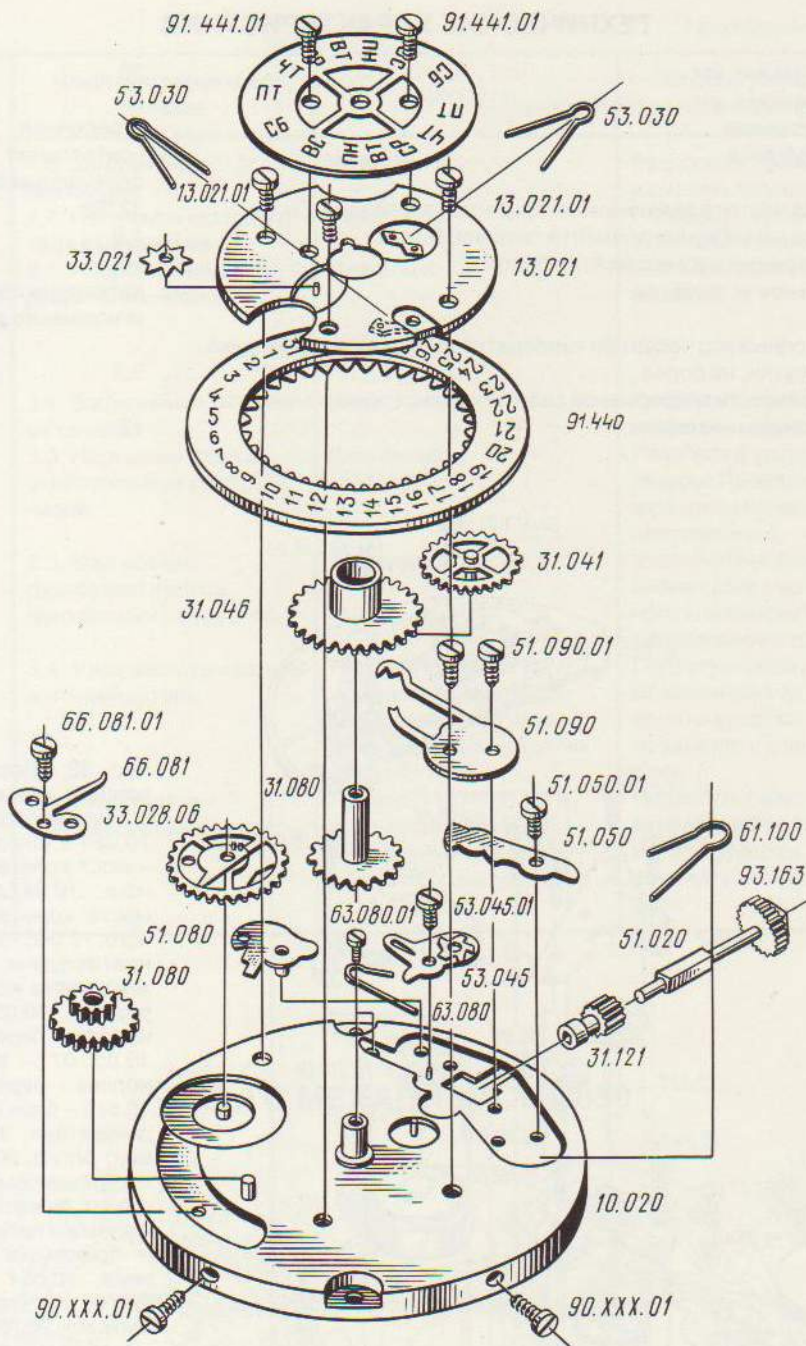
Детали и сборочные единицы календарного устройства механизма часов 3050:
